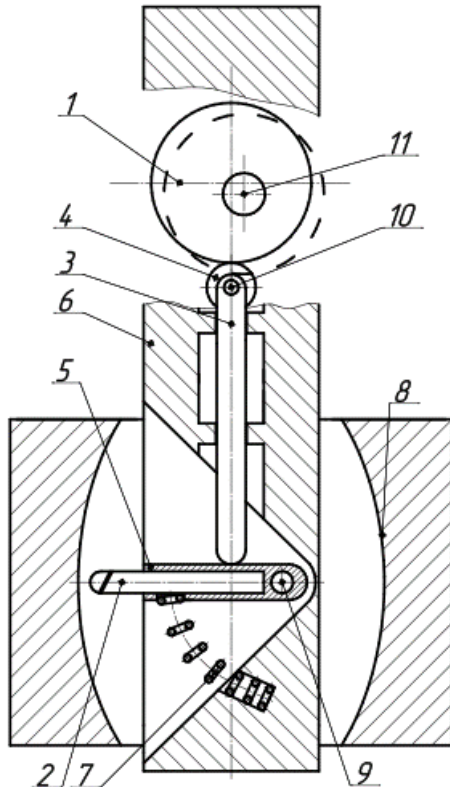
Пристосування для обробки еліпсоїда обертання: 1 – ексцентрик; 2 – різець; 3 – штовхач; 4 – ролик; 5 – тримач різця; 6 – оправка вертикально-розточувального верстату; 7 – пружина; 8 – деталь; 9 – вісь тримача різця; 10 – вісь ролика, 11 – вісь ексцентрика
